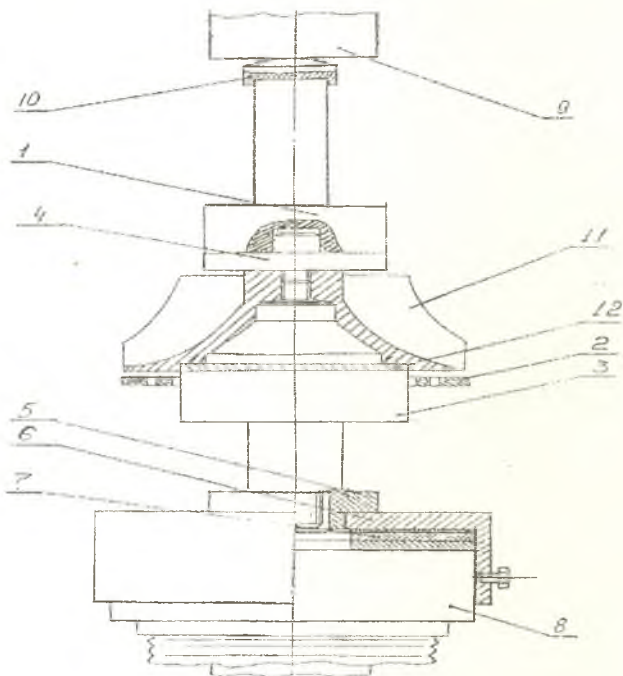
Оснастка для диффузионной сварки полых рабочих колес роторов турбин
